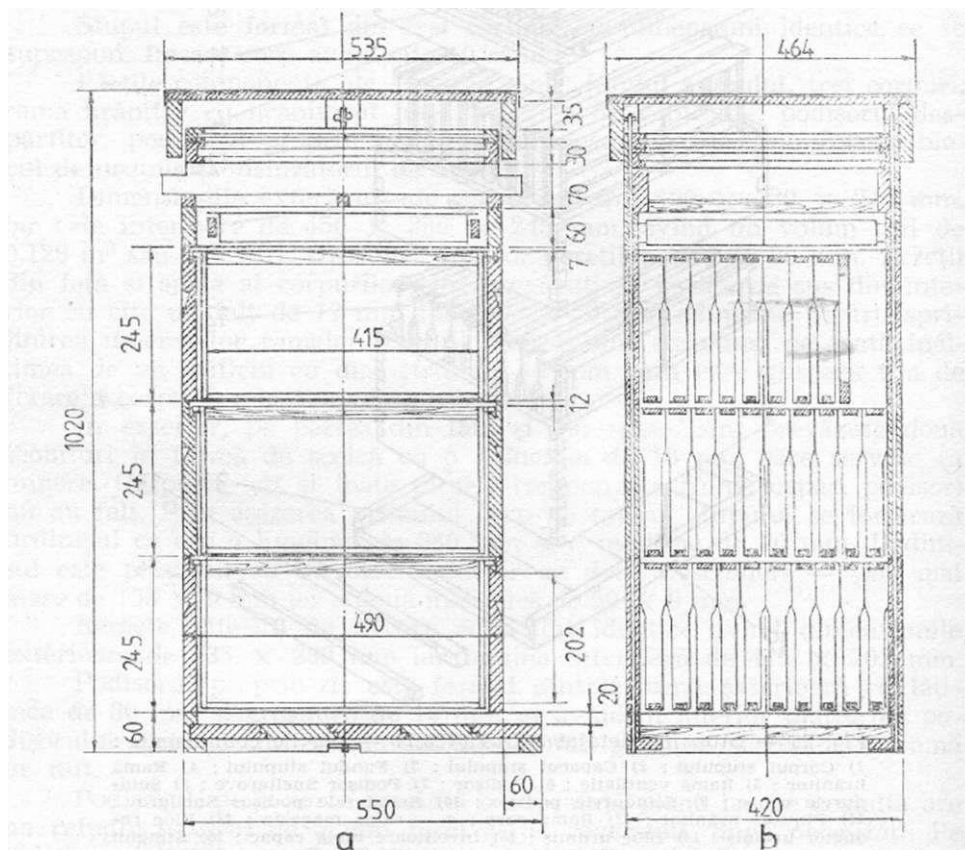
Stup multietajat STAS 8128/77 : a) Secțiune longitudinală ; b) Secțiune transversală
